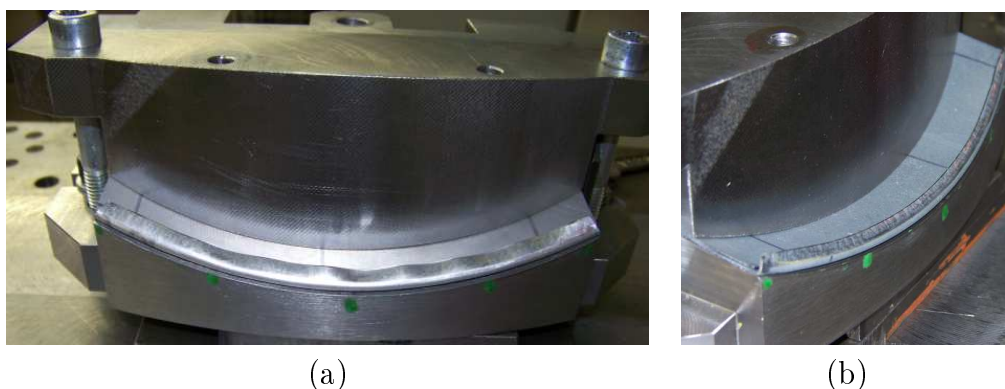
Photographies des éprouvettes R1R a) en alliage d'aluminium et b) en acier après l'opération de présertissage par roulage.
